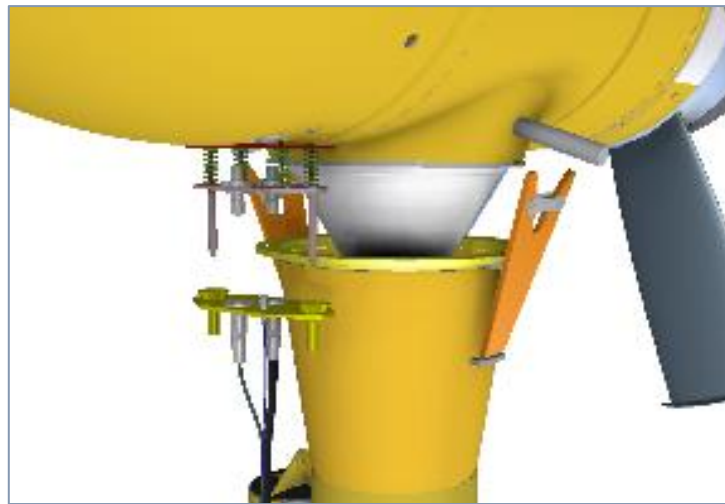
Vue 3D de principe d'une connexion wet mate passive (SABELLA)
